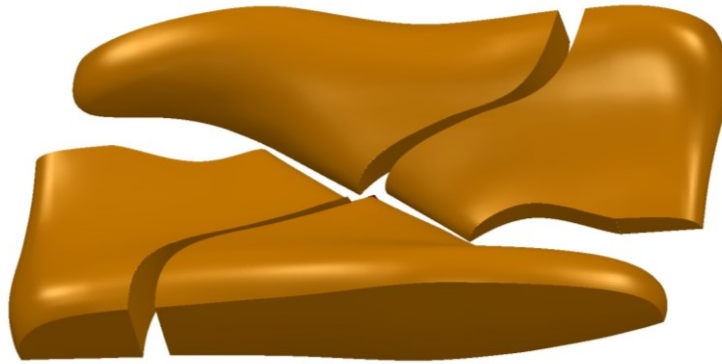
Підготовка форми колодки для фрезерування на 3-координатному верстаті з ЧПК
